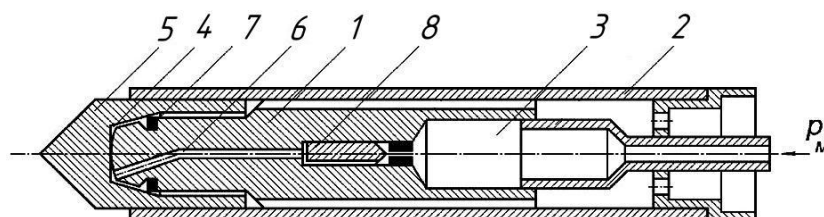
Двухклапанное пневмоударное устройство: 1 – ударная масса; 2 – корпус; 3 – камера рабочего хода; 4 – камера холостого хода; 5 – наковальня; 6 – канал; 7 – кольцевой клапан; 8 – инерционный клапан.
